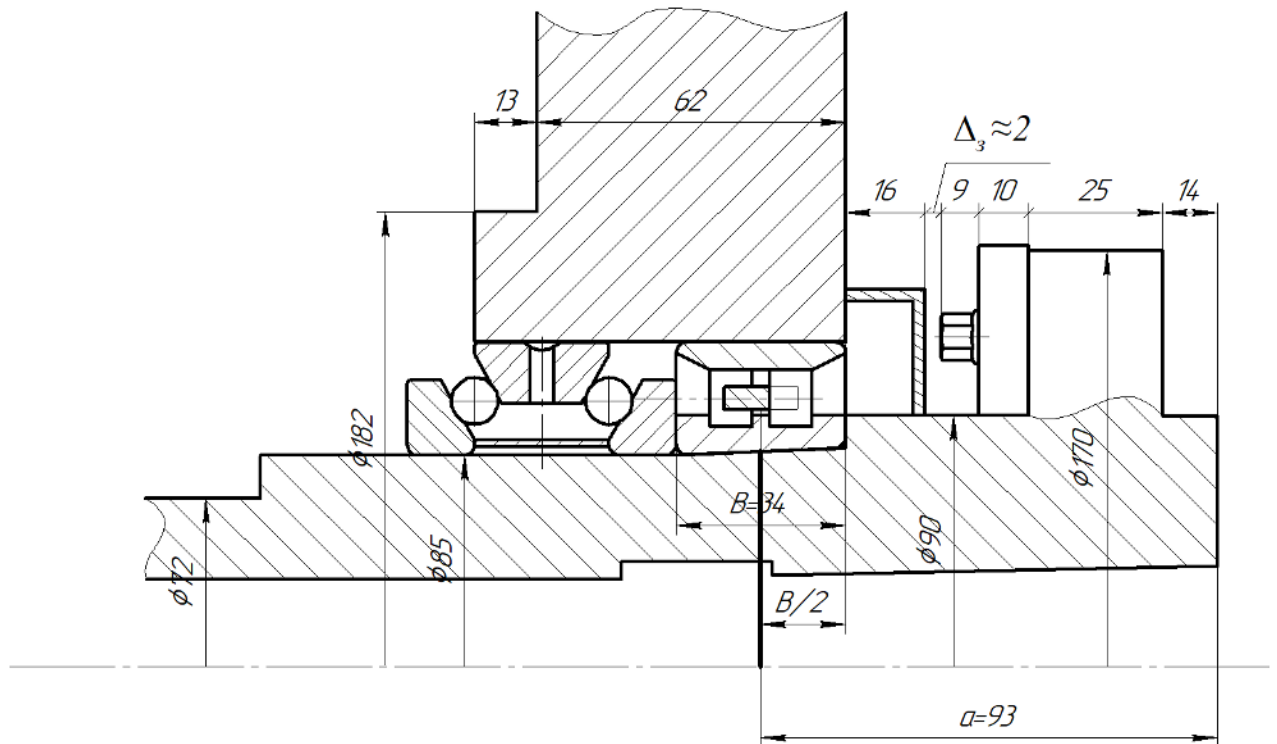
Эскиз переднего конца шпинделя исполнения Б в сборе с корпусом
